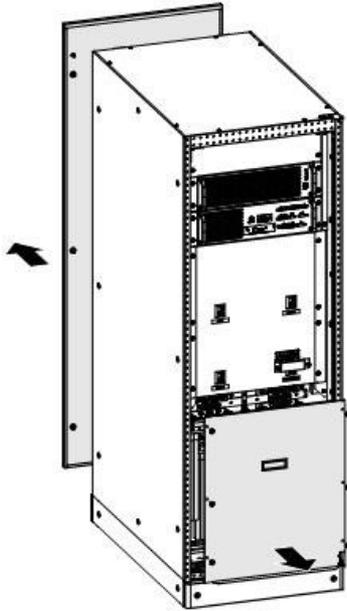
Retire la placa de cubierta del cableado de 60K, 80K, 100K, 120K
